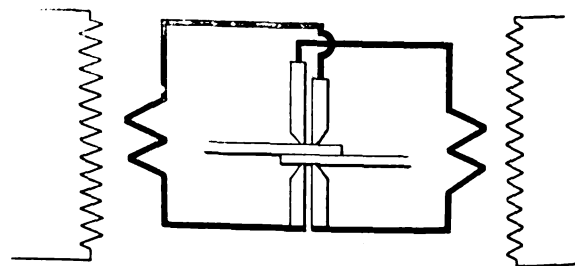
Principe de la soudure par recouvrement à deux enroulements secondaires de transformateur.
